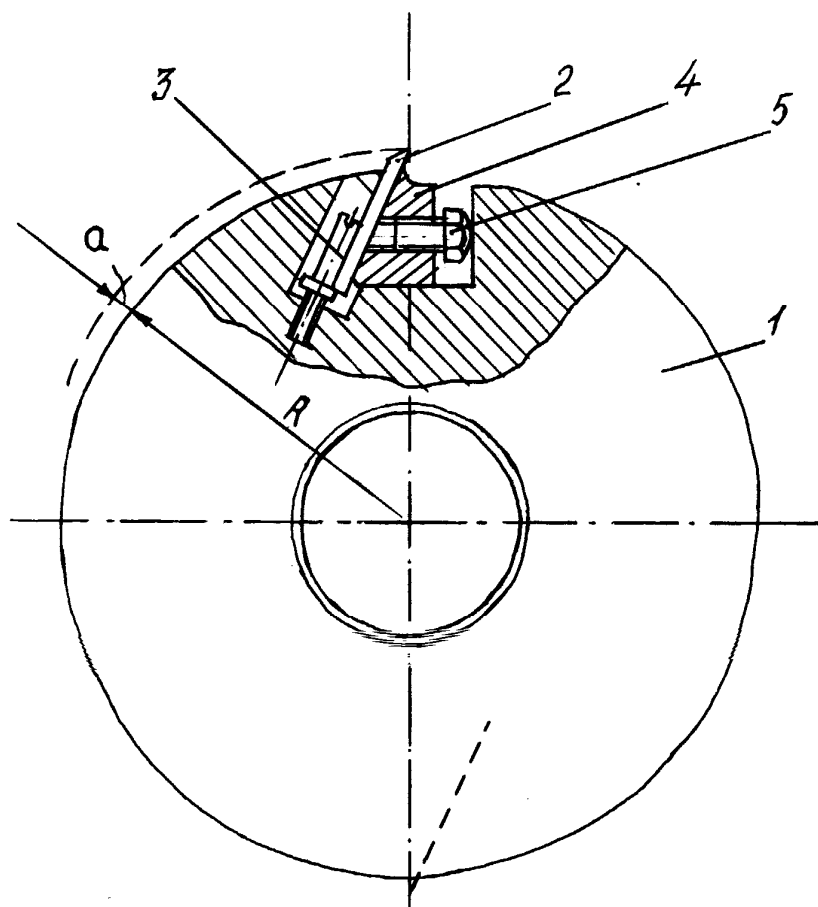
Сборная фреза с клиновым креплением призматических ножей
